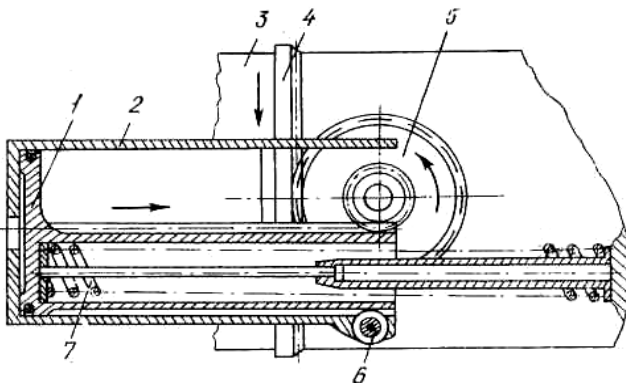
Пневматичний стартер багатоствольної зброї
